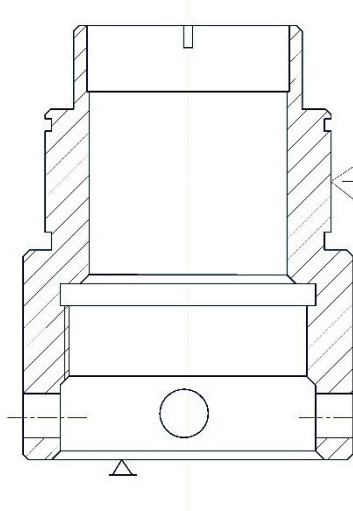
Схема базування заготовки на проміжних операціях
